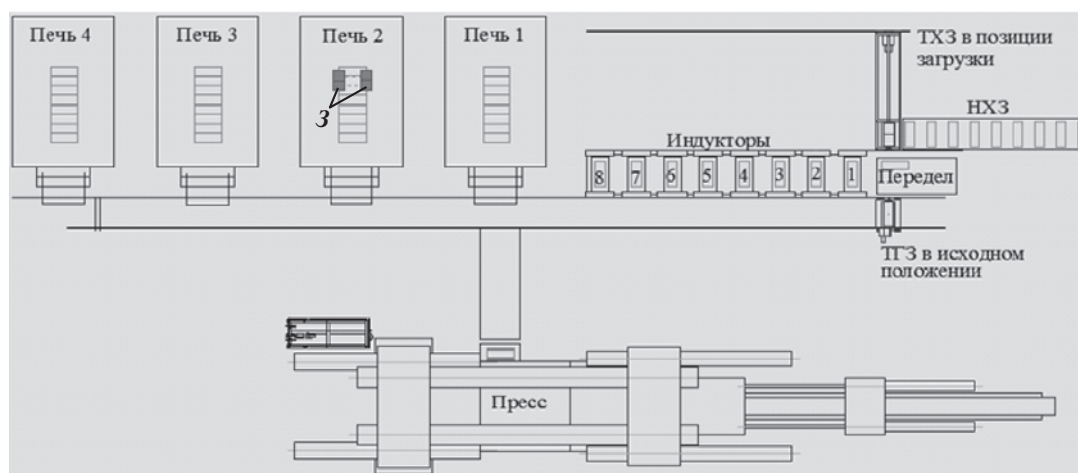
Пример схемы компоновки автоматизированного комплекса индукционного оборудования (3 – заготовка)
